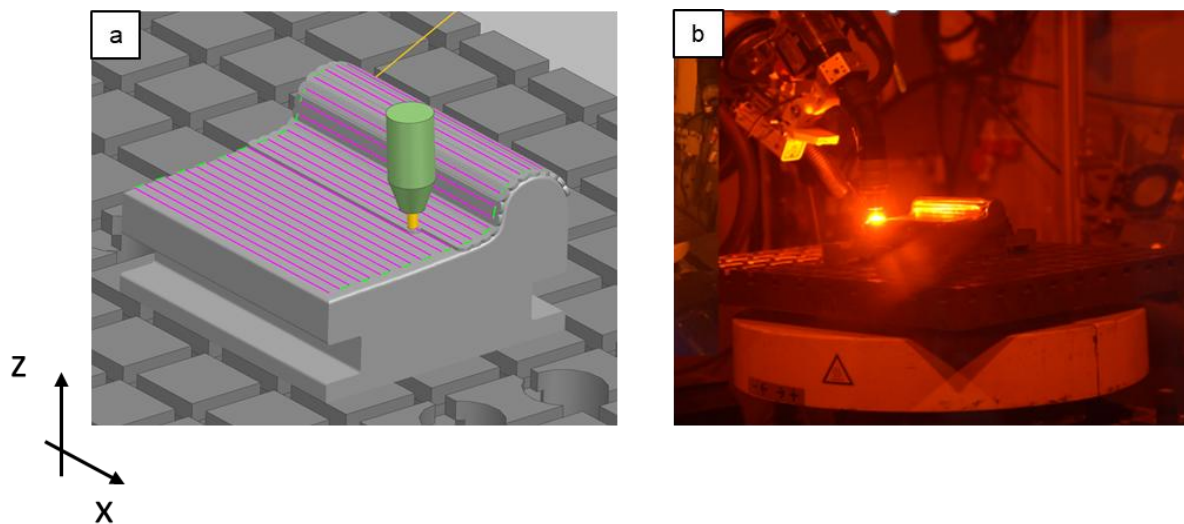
Bauteilfertigung: a) Planung der aufzutragenden Schichten im sog. linearen bidirektionalen Muster, b) Auftragschweißen am realen Bauteil mittels WAAM; z: Aufbaurichtung; x: Schweißrichtung; Bilder: Siemens
